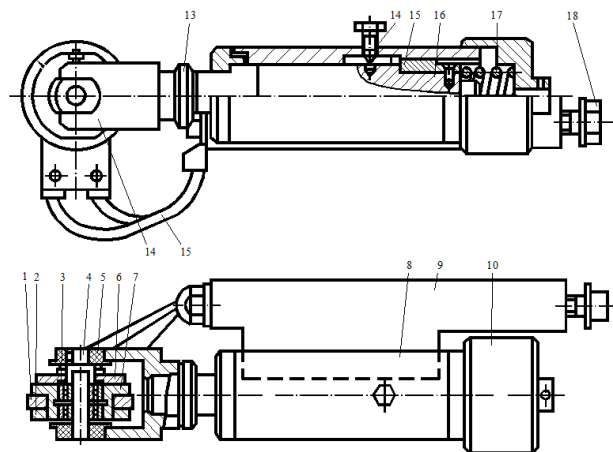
Конструкція державки для ЕМО валу турбокомпресора
